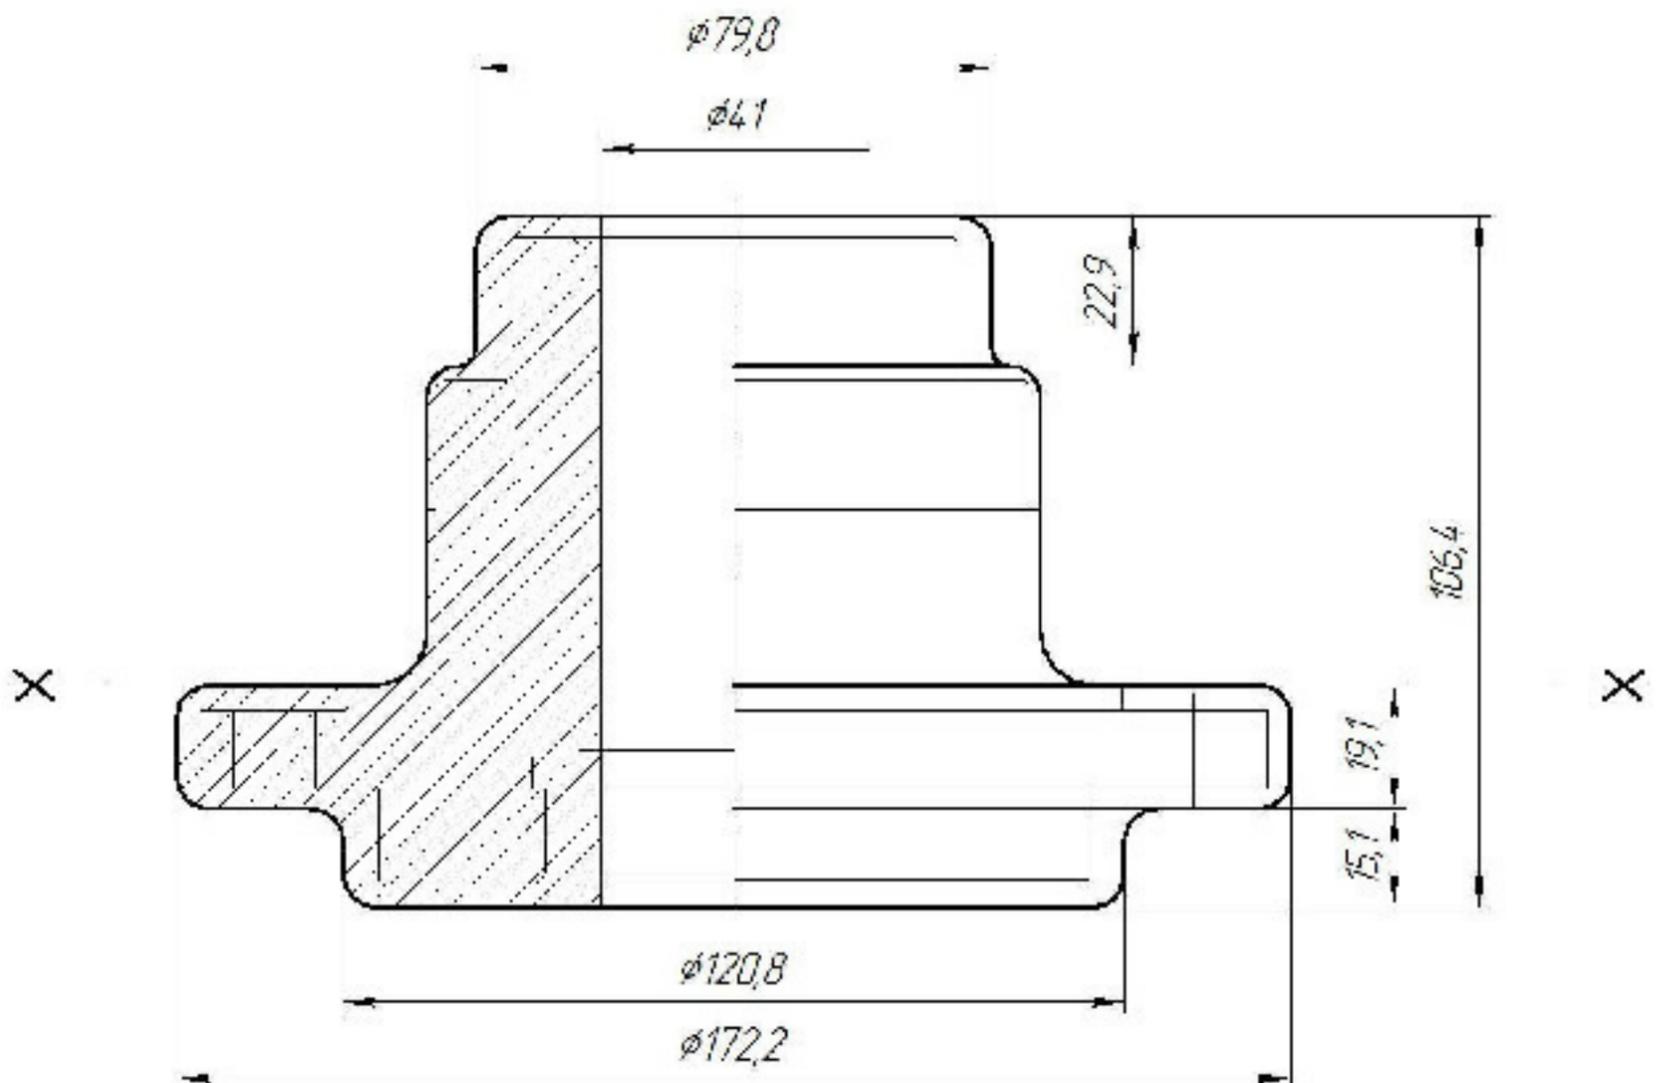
Ескіз заготовки при литті в піщано-глинисті форми (з машинним формуванням суміші)
